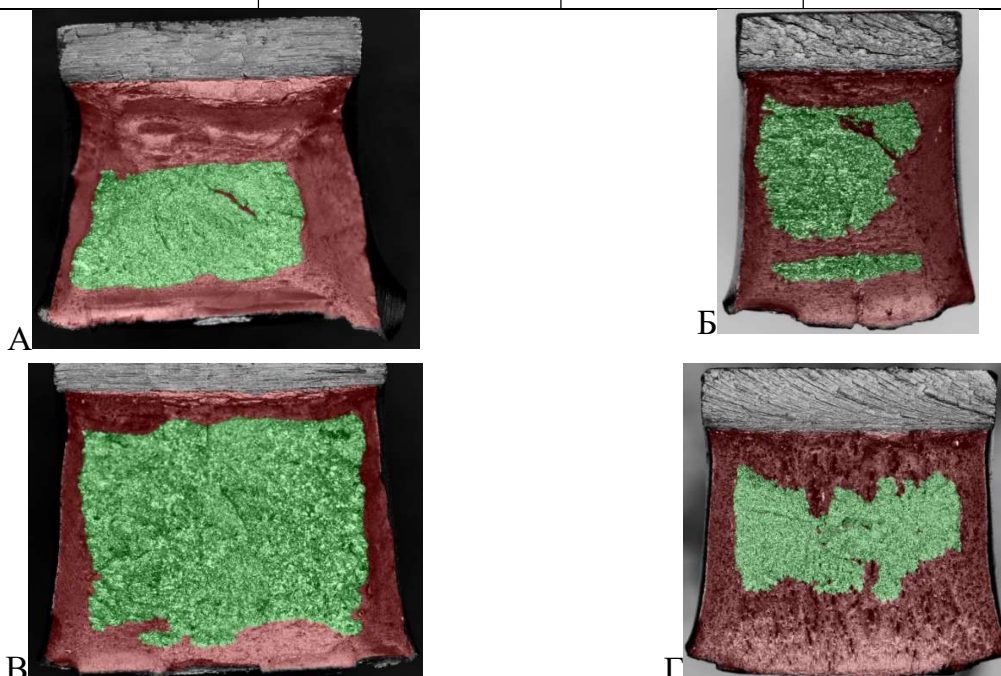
Изображения изломов после выделения на них областей с вязким и хрупким изломом свёрточной нейронной сетью (а – образец сварного соединения, б – образец околошовной зоны стали 17Г1С, в – образец стали 09Г2С ТУ, г – образец стали 17Г1С)
